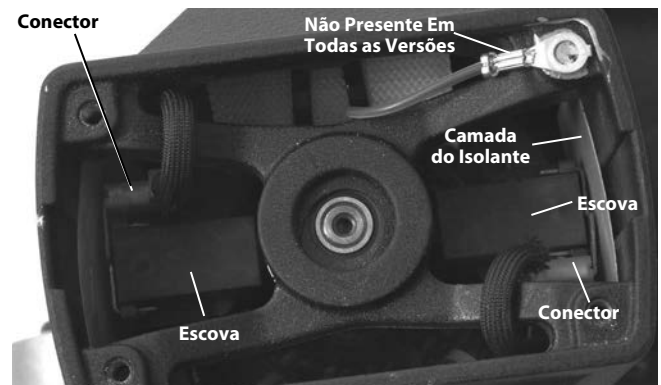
Colocação da Escova - Tampa do Motor Removida
